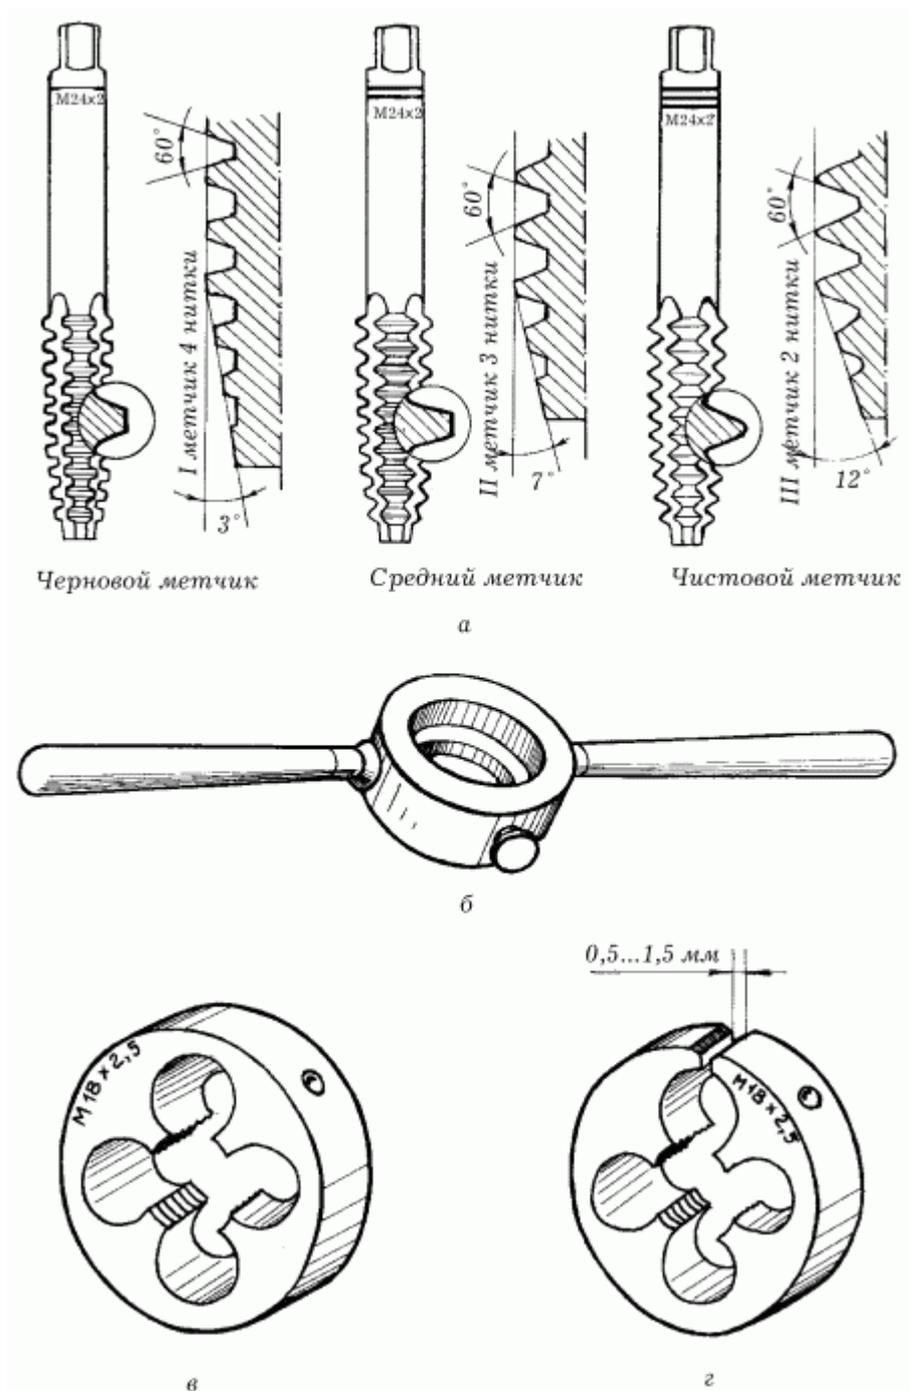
Приспособления для нарезания резьбы: а – набор метчиков; б – вороток для метчика; в – круглая цельная плашка; г – круглая разрезная плашка.
